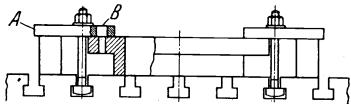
Werkzeugbefestigung an der Maschine. A Klaue, B Loch für Stift zur Sicherung gegen Verdrehen.
